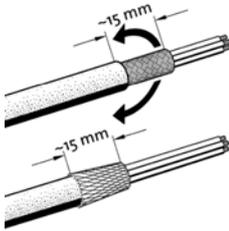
Colocación de apantallamientos de cables en los racores atornillados para cables CEM (SC...FC WM)
